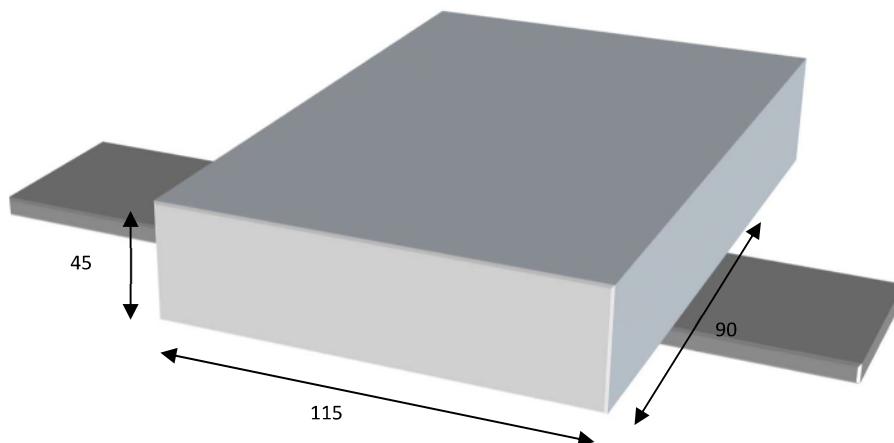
Dimensiones máximas (mm) de montaje en carril DIN
